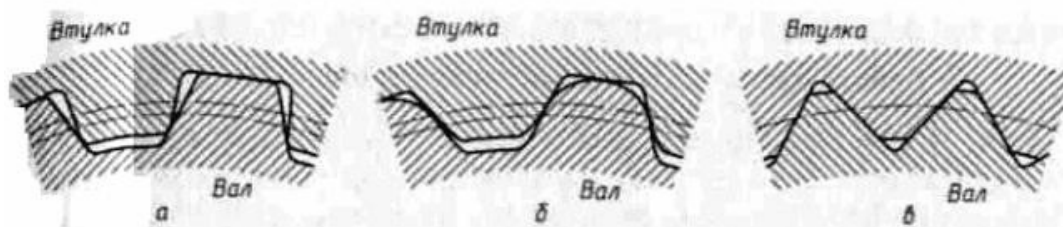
Типы шлицевых соединений: а - прямобоочное; б - эвольвентное; в – треугольное
